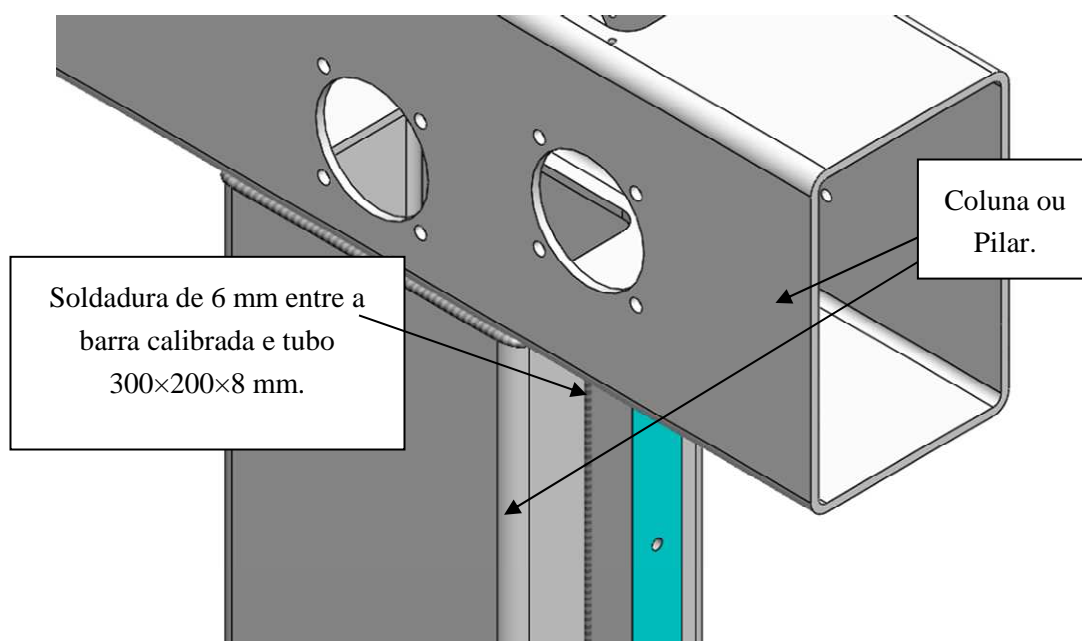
Cordão de soldadura barra calibrada.
